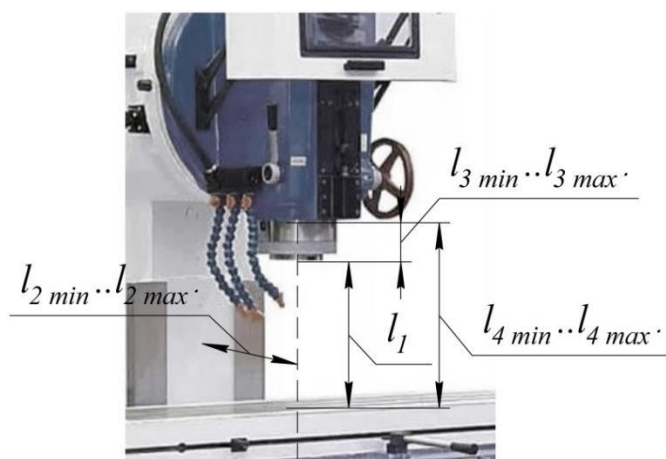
Эскиз рабочей зоны вертикально-фрезерного станка
